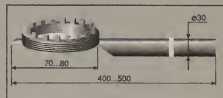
Приспособление для отворачивания регулировочных гаек.
